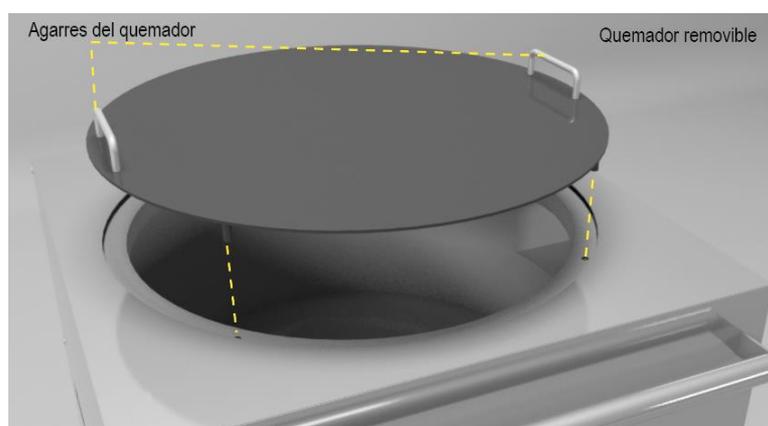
Plancha/quemador removible con sus puntos de anclaje.
